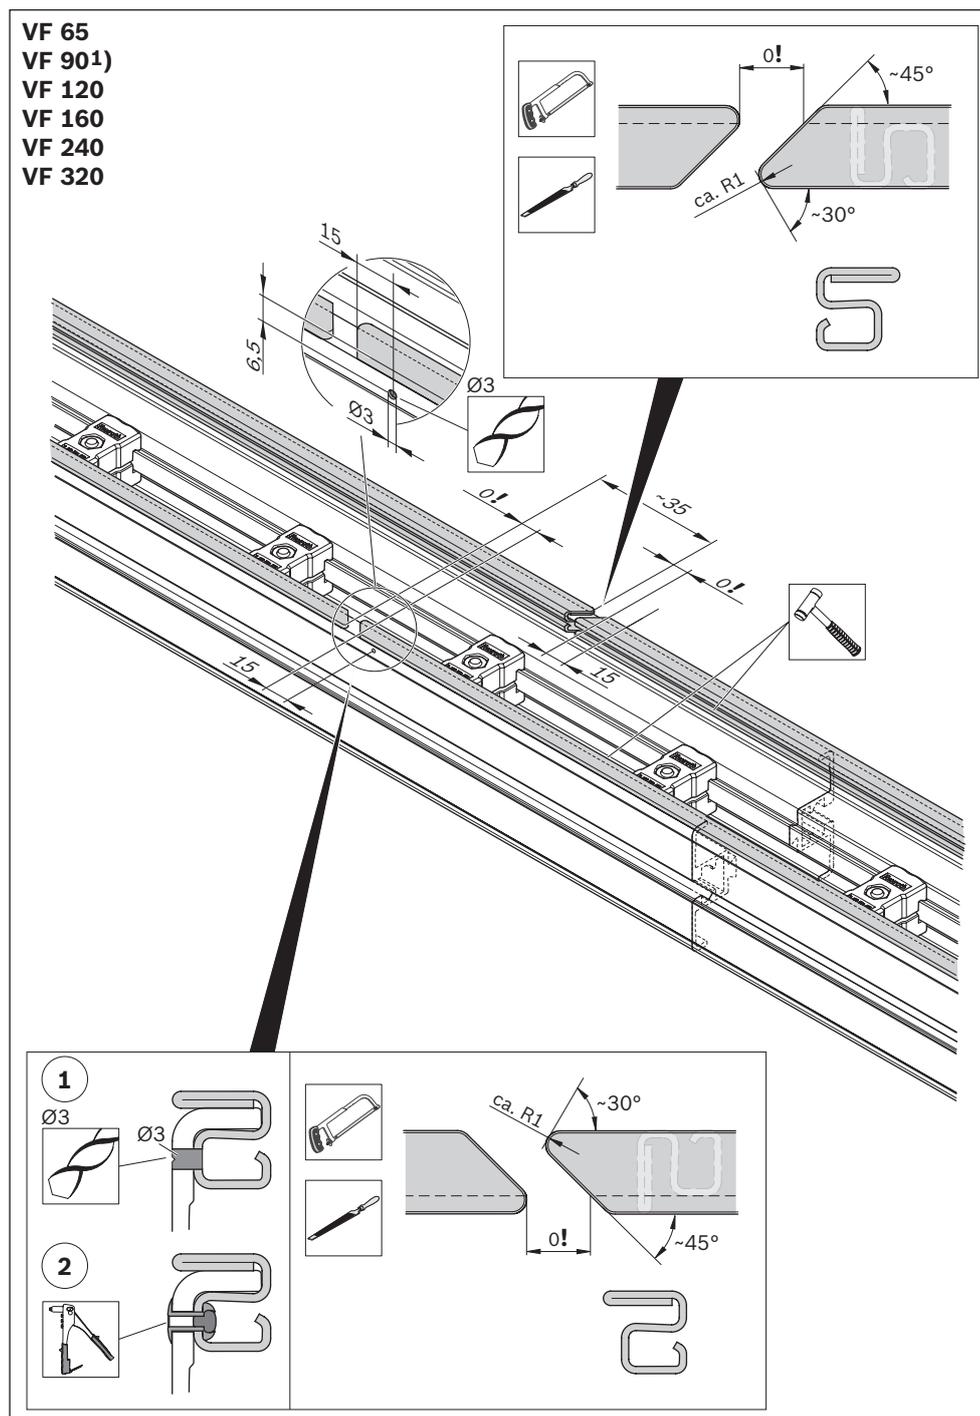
STS-Gleitleiste montieren, Streckenprofil
